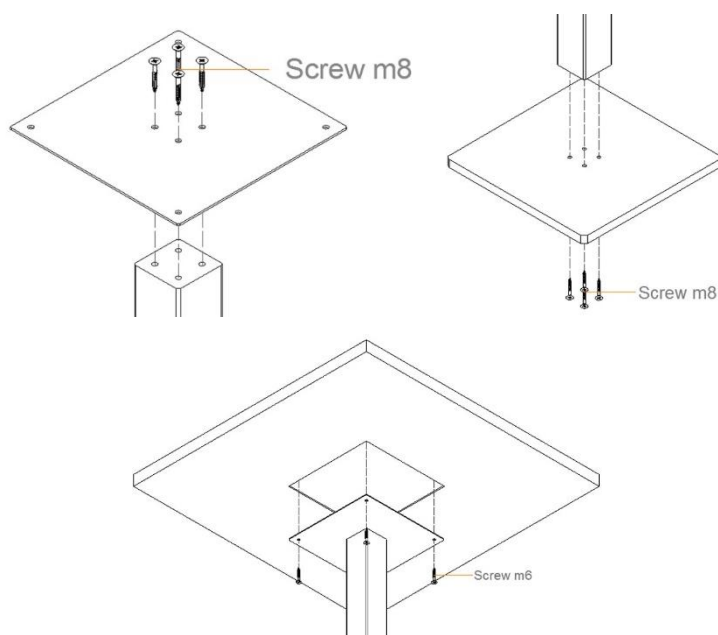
Desenho técnico de pormenores de encaixe e união da mesa.
